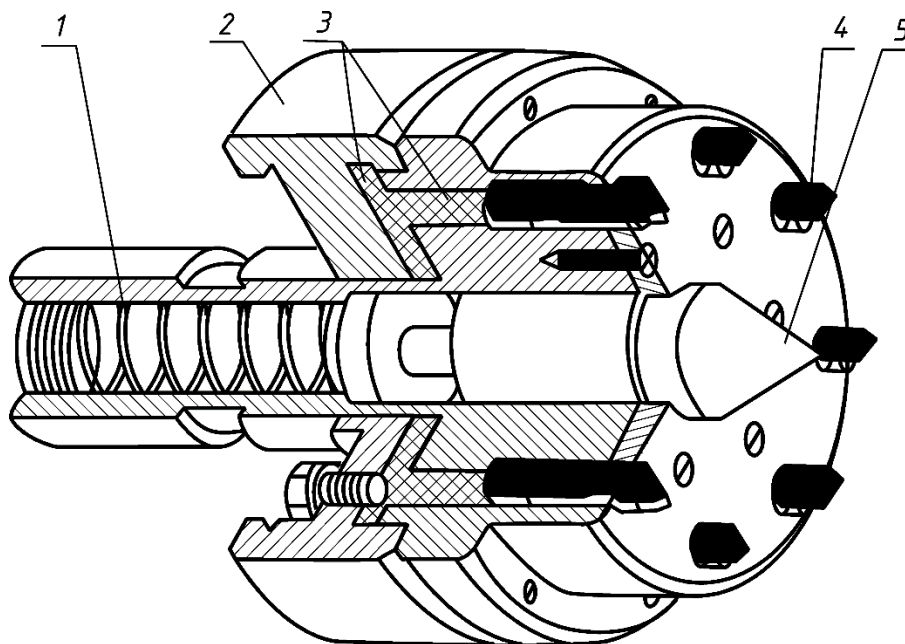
Поводковый патрон с плавающими ножами: 1 – пружина; 2 – корпус; 3 – гидропласт; 4 – нож упора; 5 – центр
